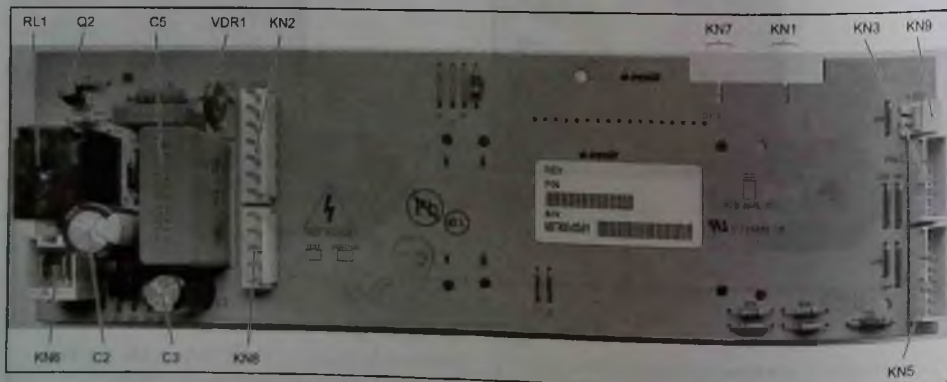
Внешний вид ЭМ, его основные компоненты и соединители (вид сверху)
